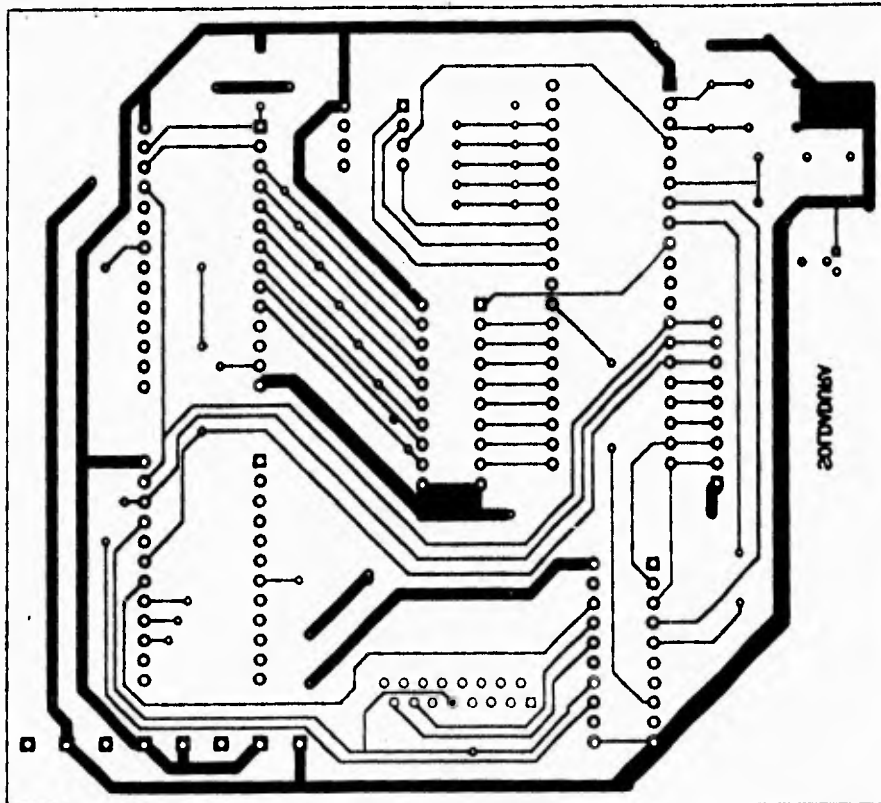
Cara de soldadura del circuito impreso de la lógica de control.
